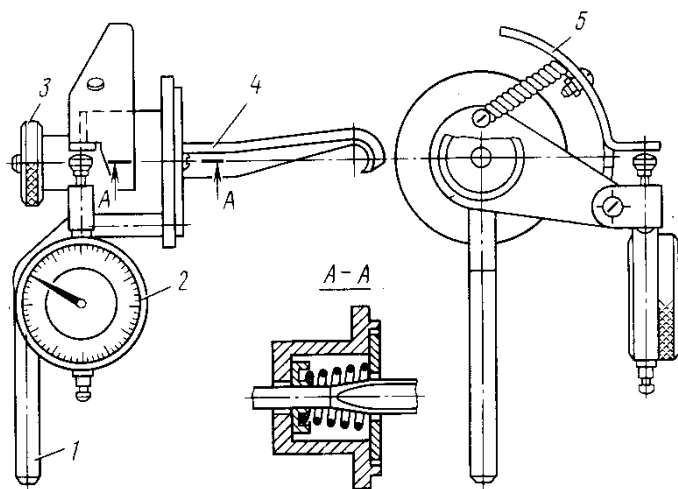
Приспособление для проверки зазора в шестернях главной передачи
